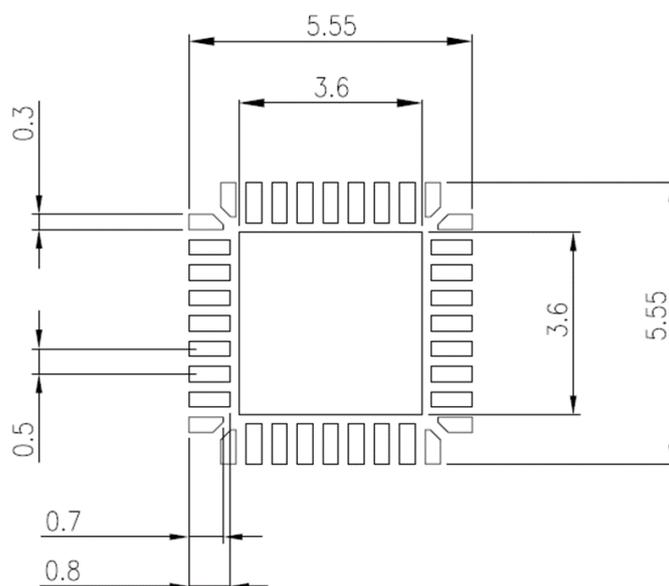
P-WQFN36-0505-050-001 参考フットパターン例
